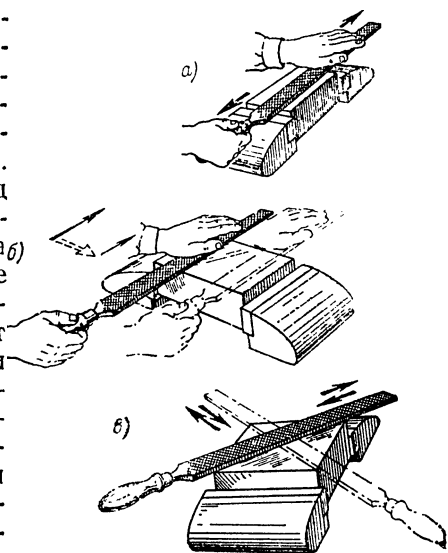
Движения напильника при опиливании плоских поверхностей
